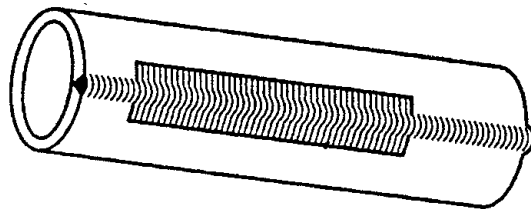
Випробний зразок зварних труб з поздовжніми швами
